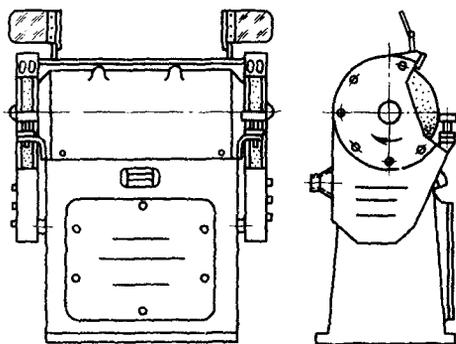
Обдирочно-заточный станок 3М-634Д
